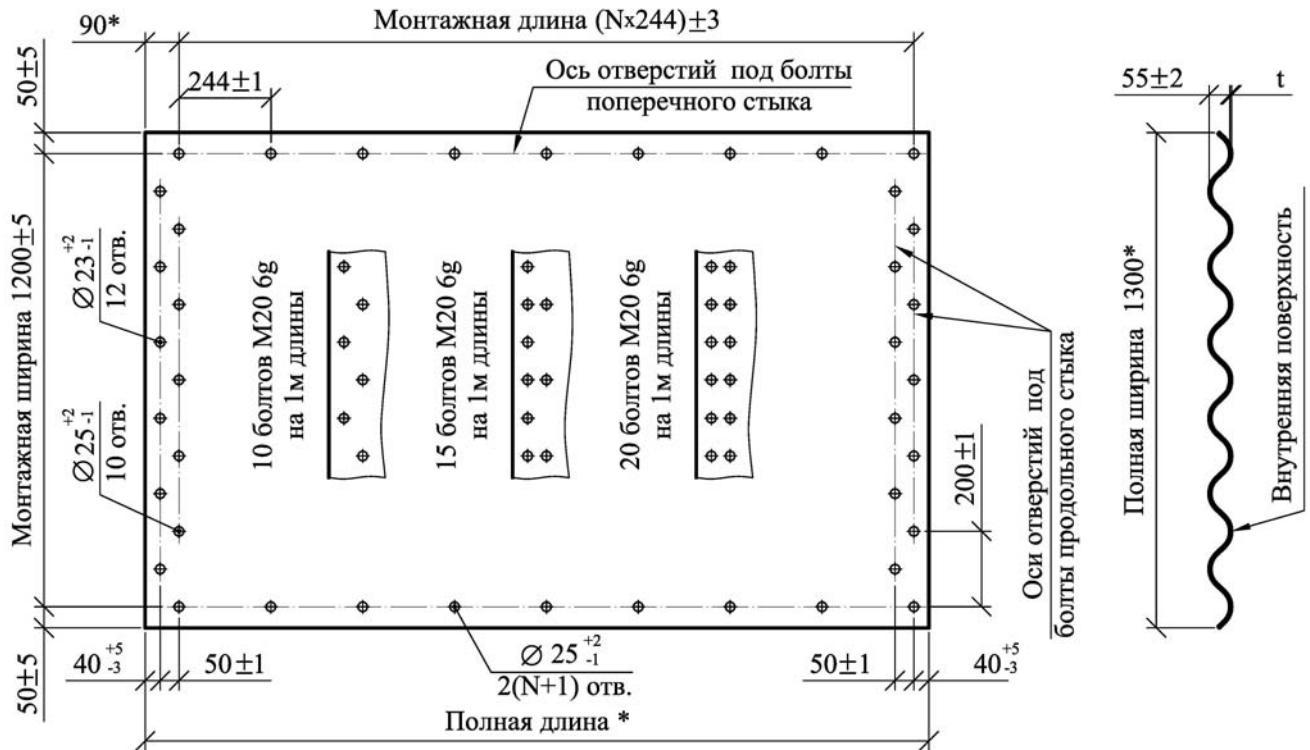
Гофрированный стальной лист ГЛ55. Вид и размеры
